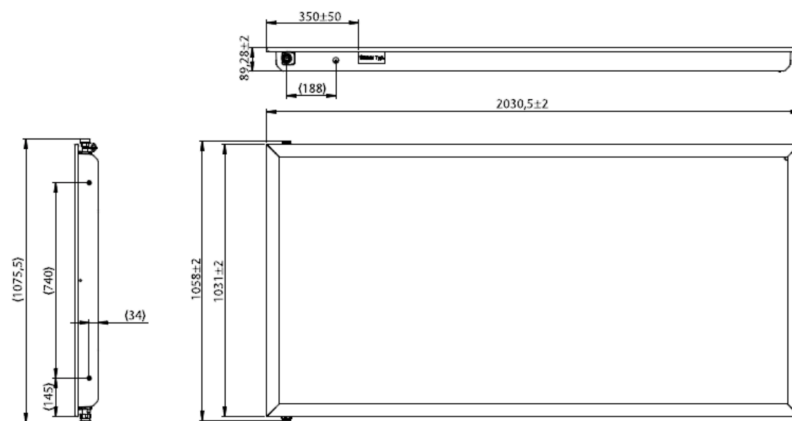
Dimensiones captador solar plano TERMICOL T20US.
